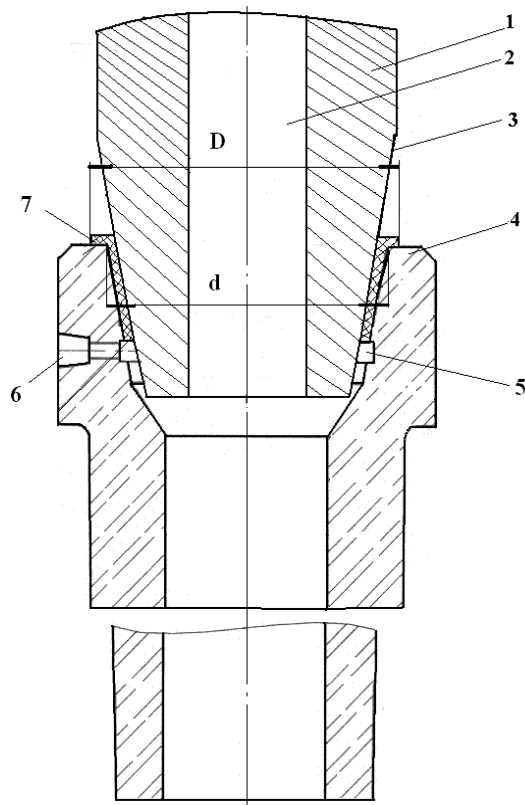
Устройство для защиты струи металла при разливке на МНЛЗ
